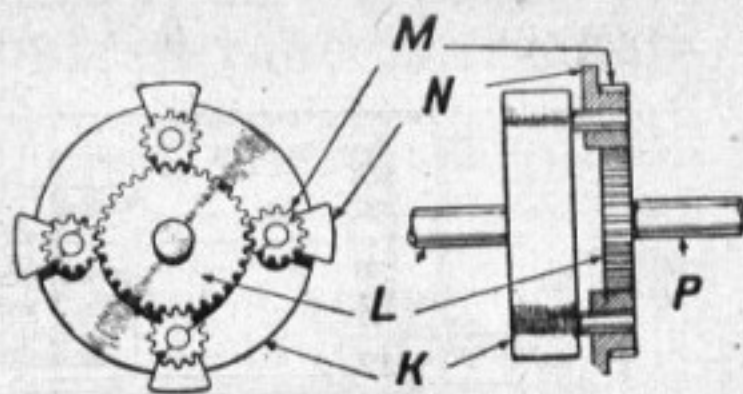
Принципиальная схема автоматической коробки передач Хоббс
